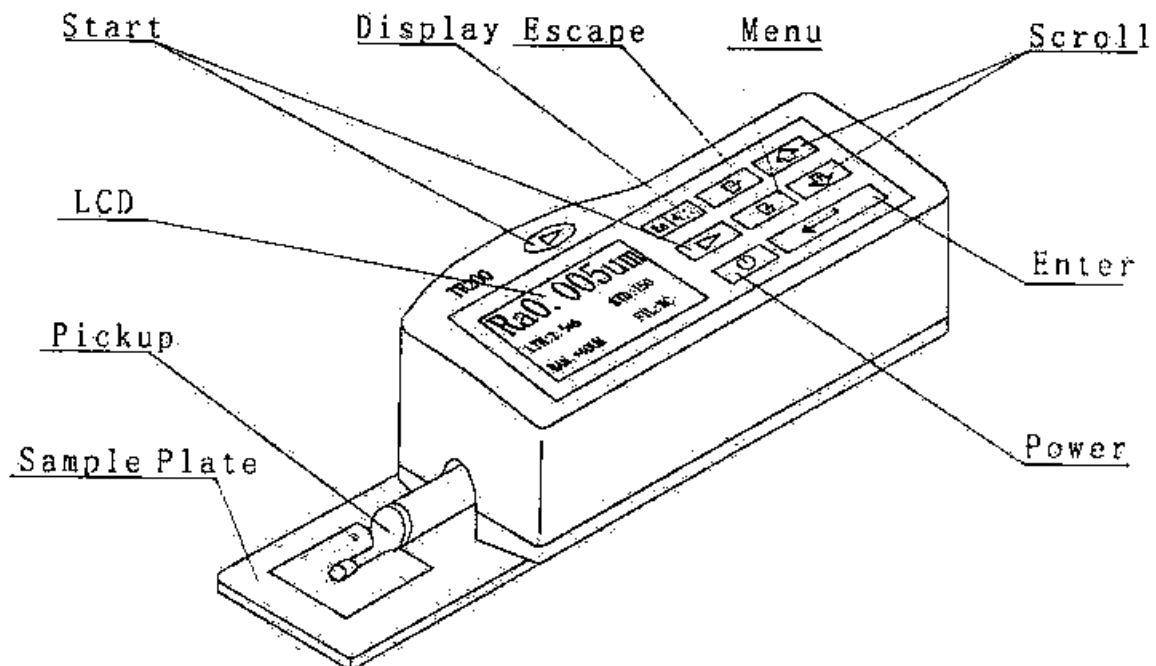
Внешний вид портативного измерителя шероховатости TR-200:
